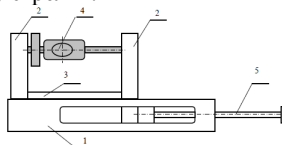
Схема установки индикаторного нутромера на заданный размер
